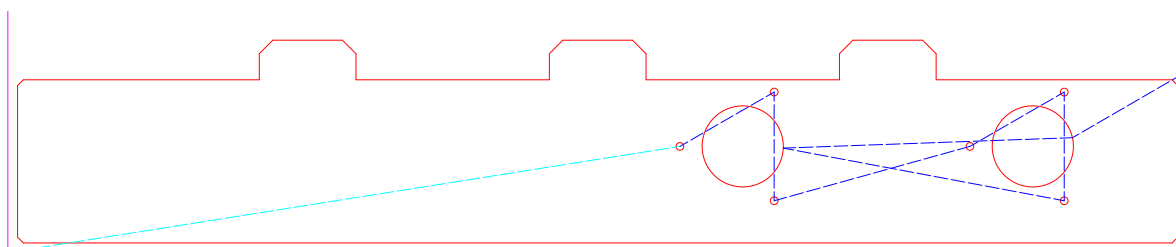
Tvar součásti převedený do dxf formátu.
